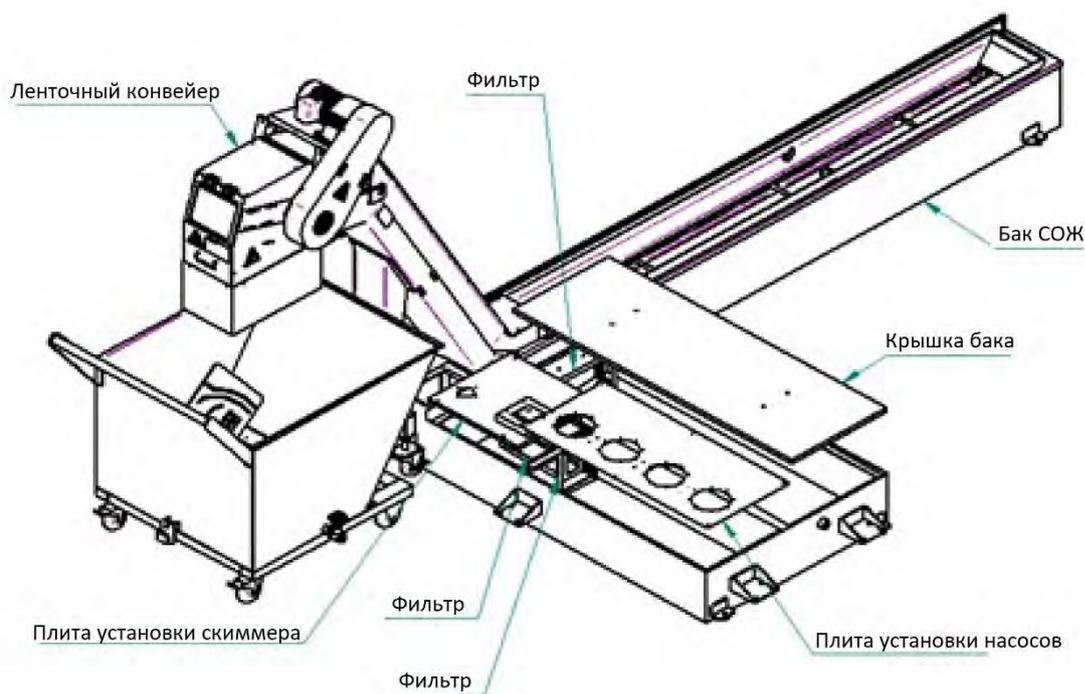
чертеж расположения устройства подачи СОЖ
